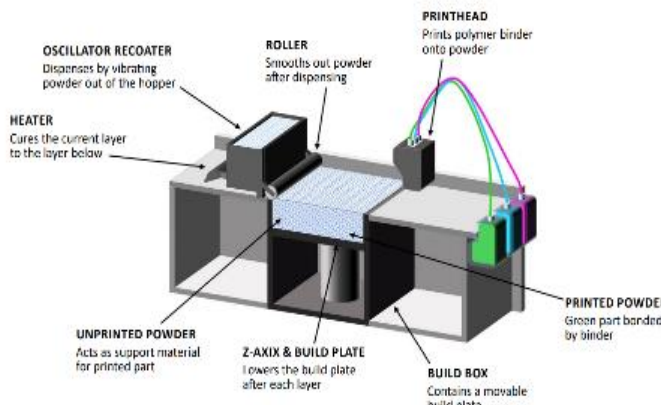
e 10 Schema di funzionamento Binderjetting ed oggetto stampato
